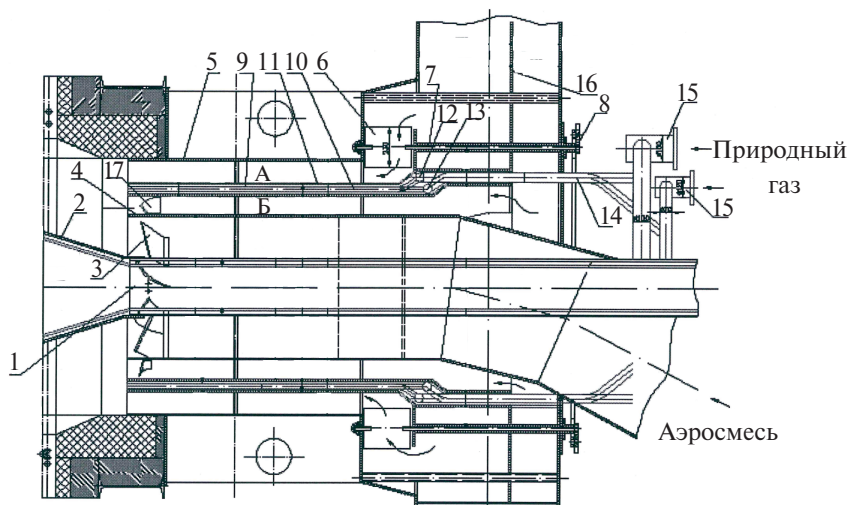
Конструктивная схема пылегазовой горелки котла П-57:
